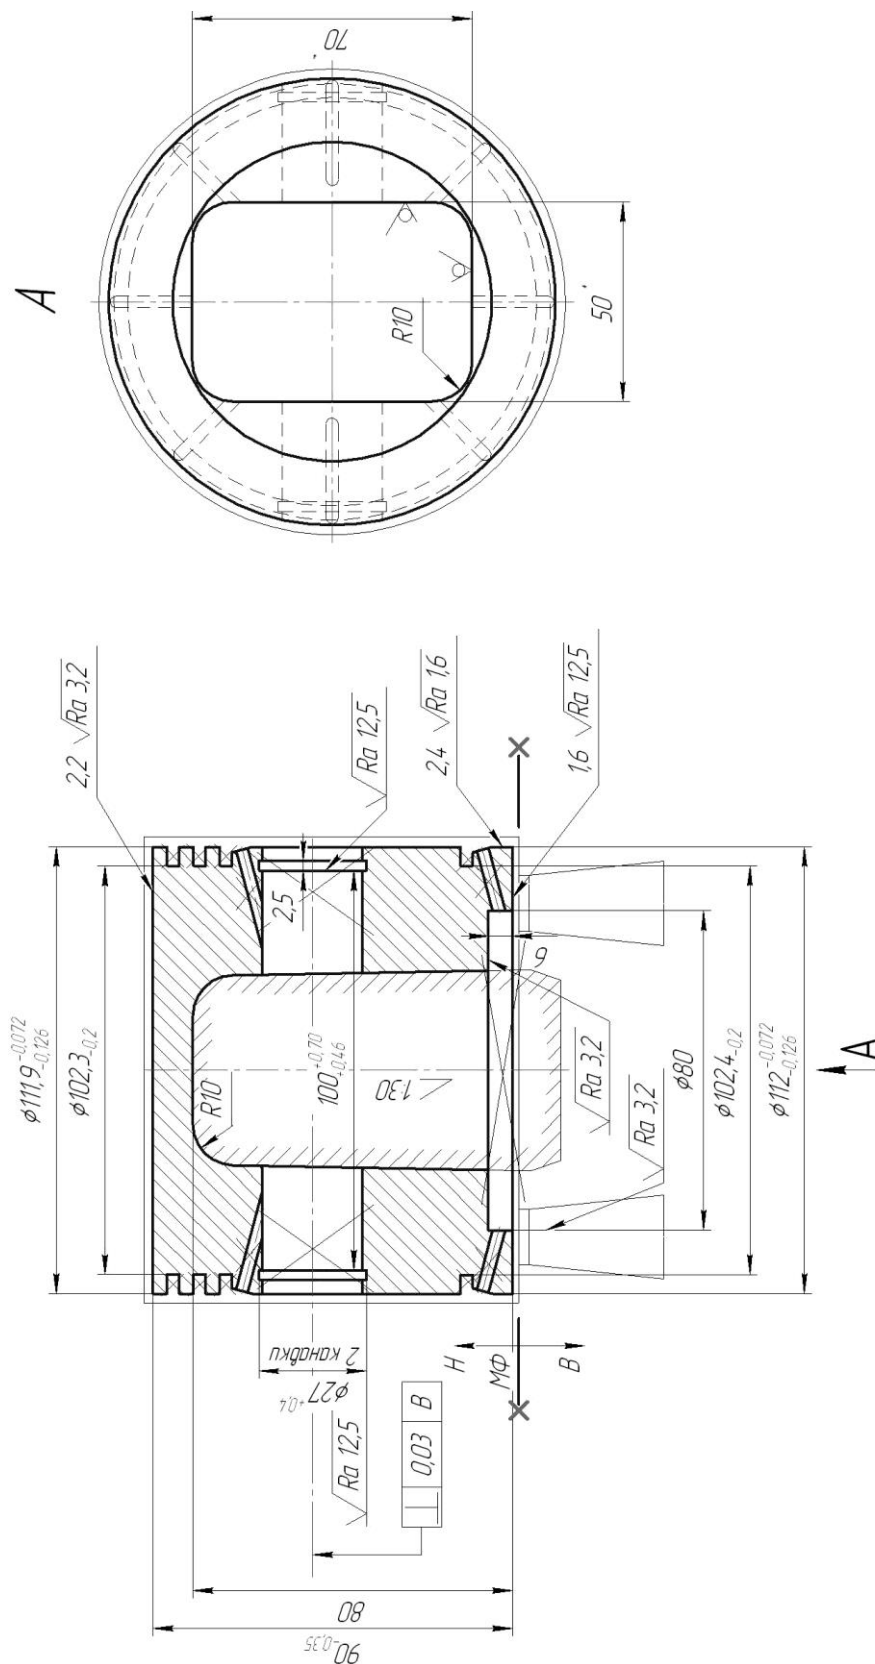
Суміщене креслення деталі поршень компресора (відливка в оболонковій формі)
